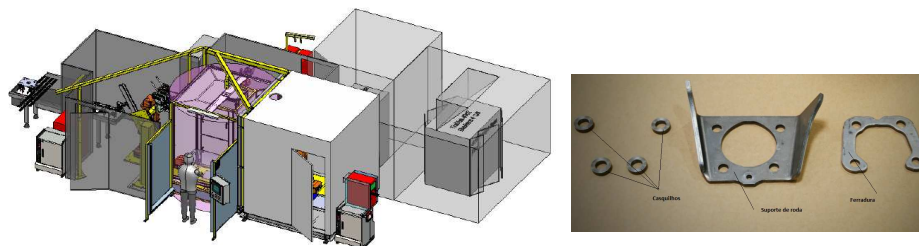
Vista geral do equipamento de soldadura e peça a fabricar [AWL 2012]
